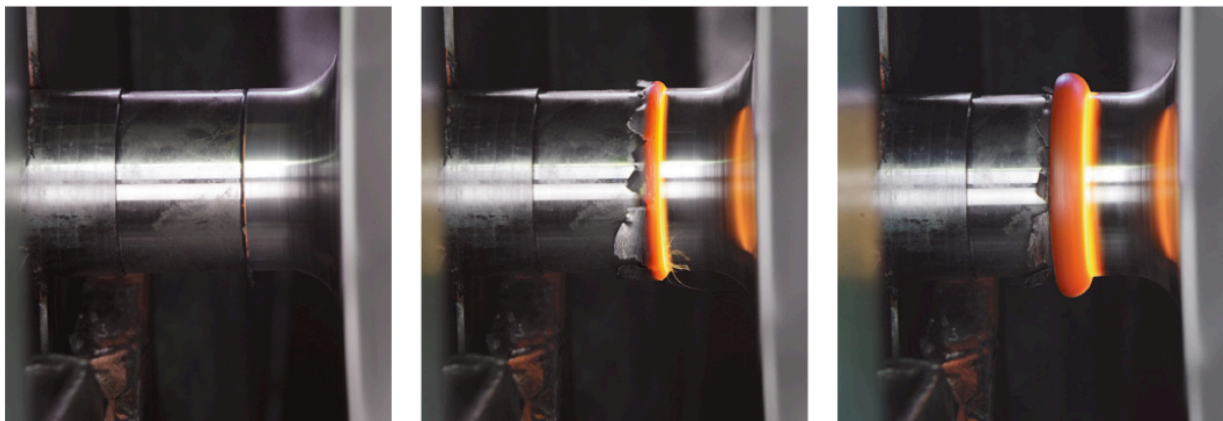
Fases proceso de soldadura por fricción rotacional. [34]
